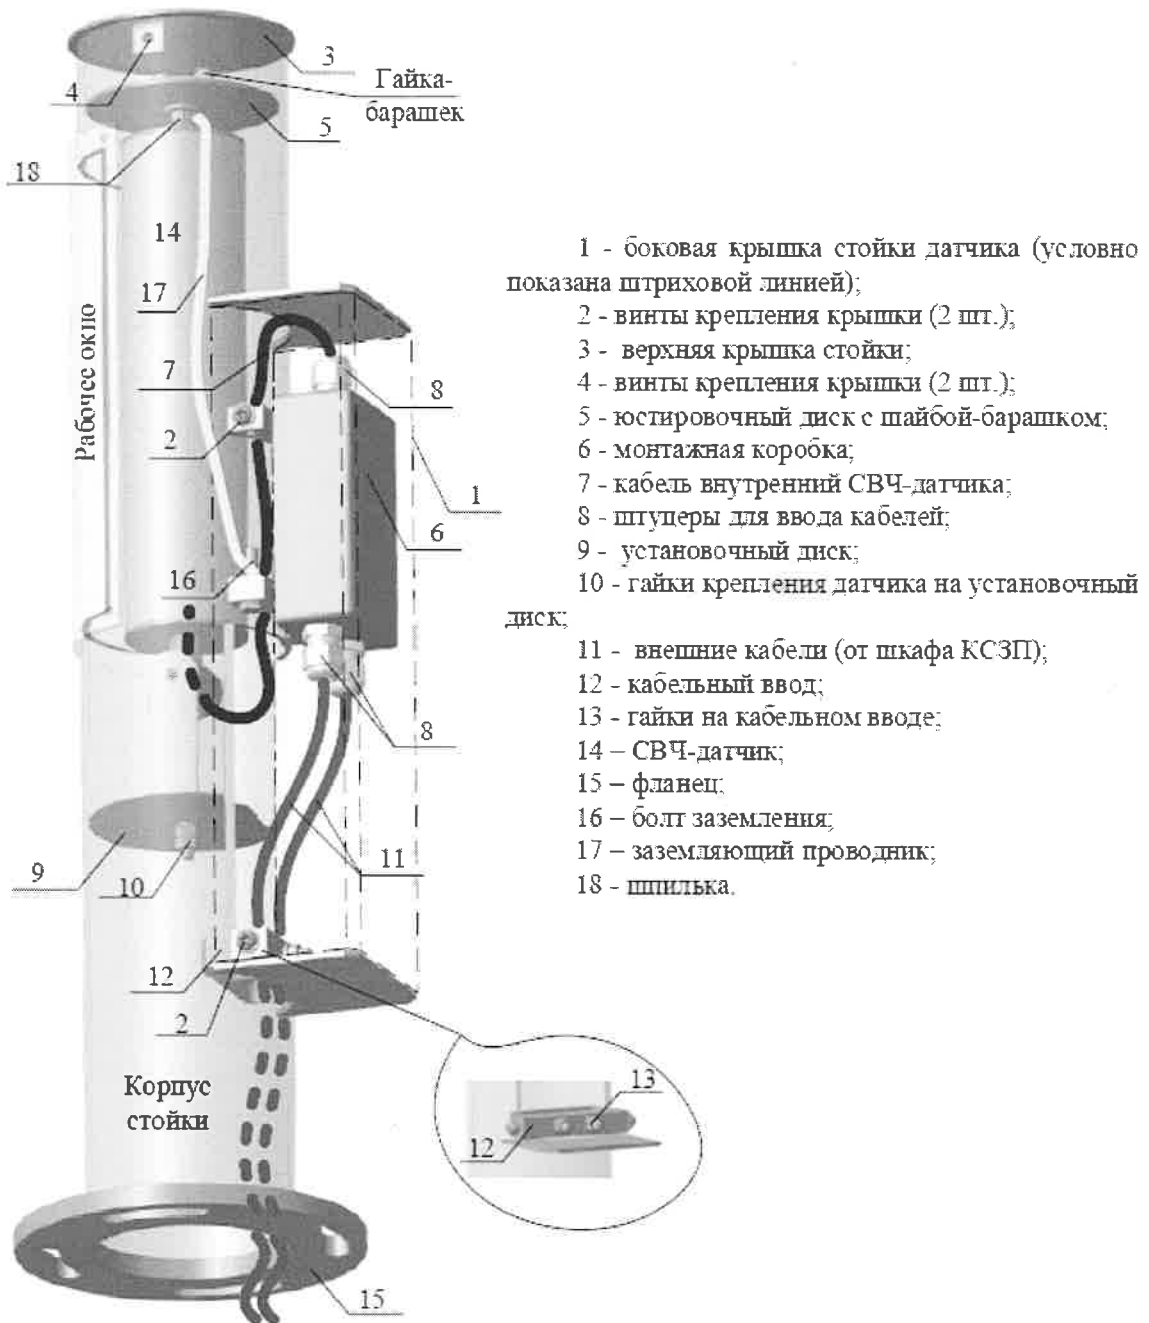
Крепление датчика внутри стойки СВЧ
